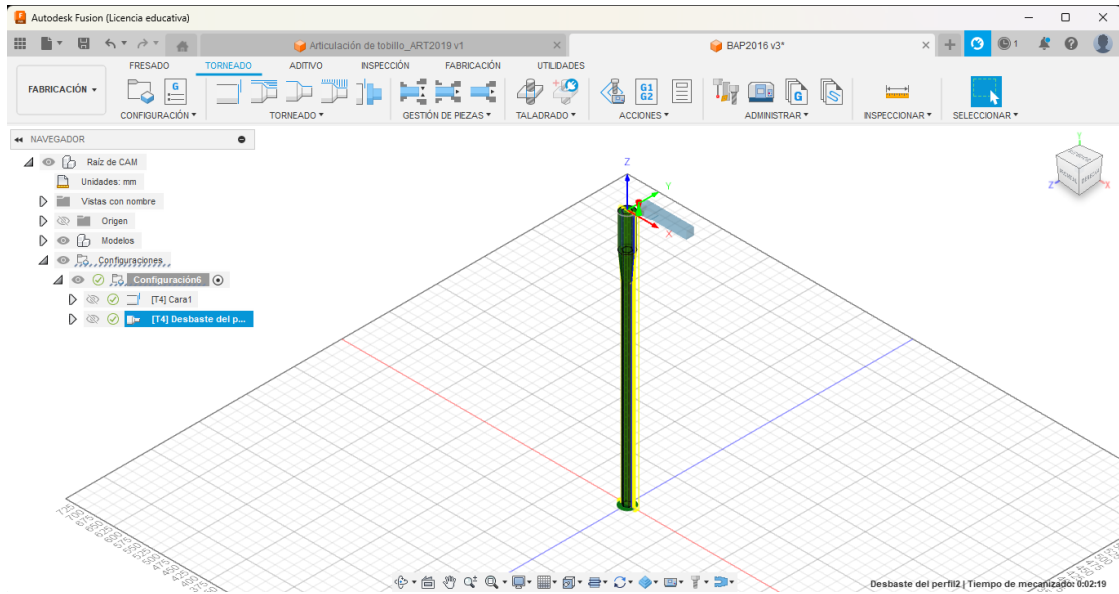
Maquinado de la pieza Barra de pantorrilla BAP2016
